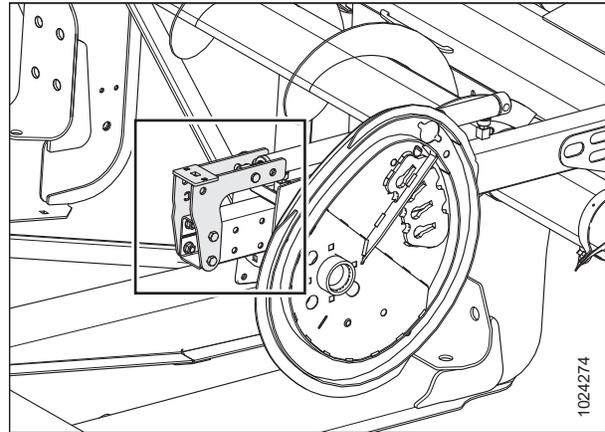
Mittlerer Haspelarm – Bauform links und rechts ähnlich
